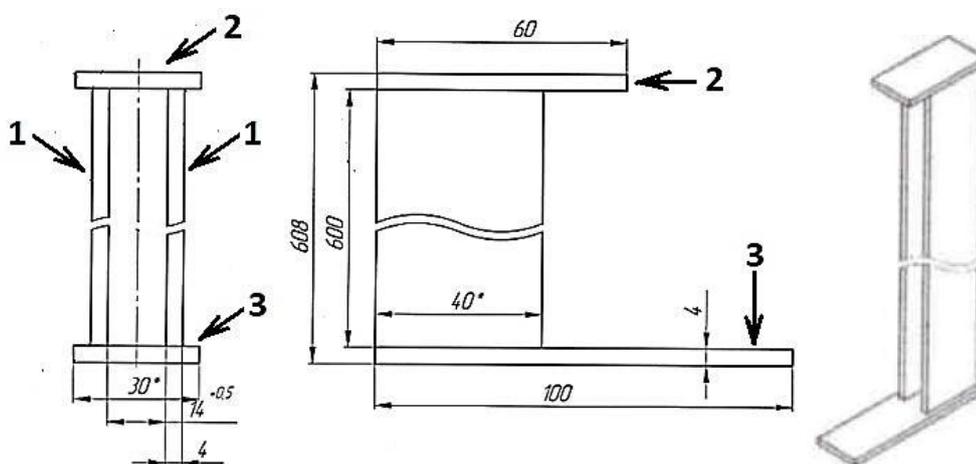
Конструкция и размеры кронштейна УККП-60 с опорными пластинами:
